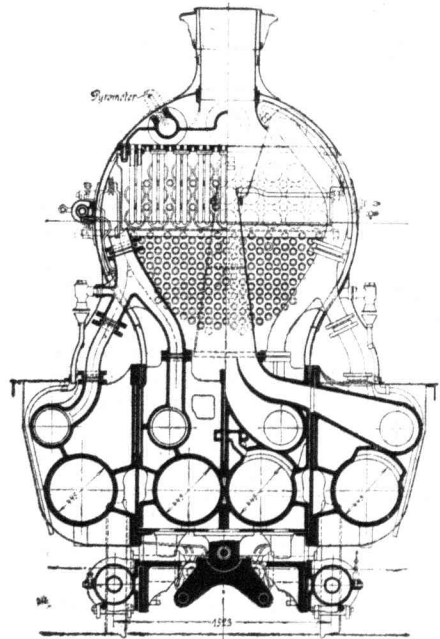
Querschnitt durch die Dampfzylinder der 2 C-Heißdampflokomotive.
